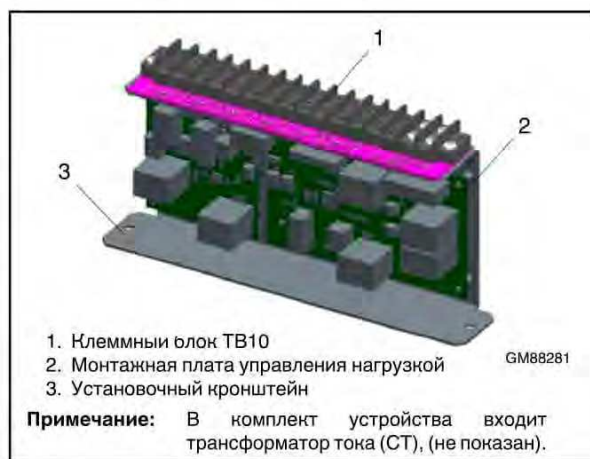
Устройство сброса нагрузки GM88281-1 (устанавливается в корпусе переключателя резерва)
